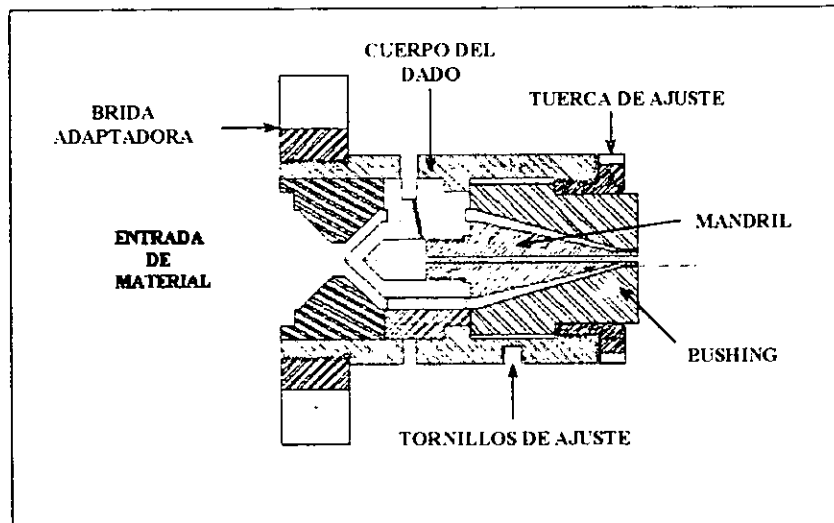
Dibujo de ensamble de un dado para tubo.
